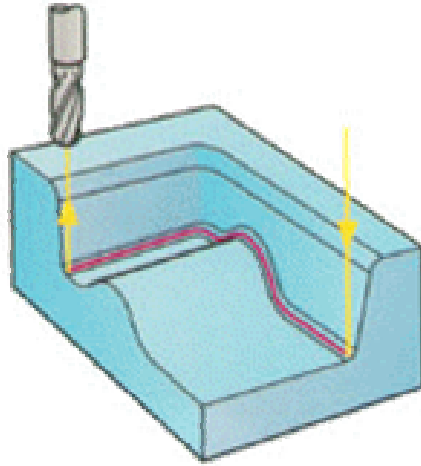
Üç boyutlu ofset spiral finiş işleme [1]
